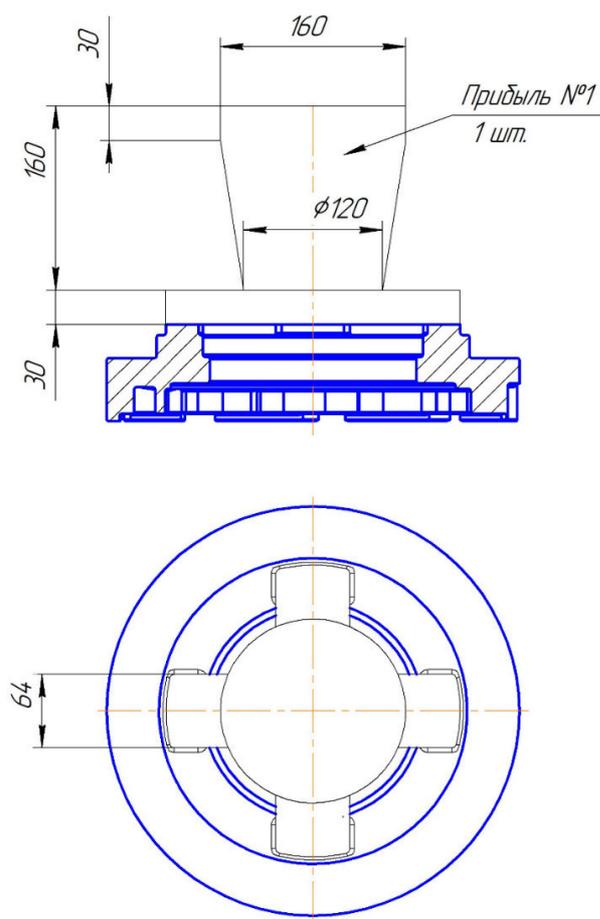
Эскиз отливки с прибылью и литниковой системой
